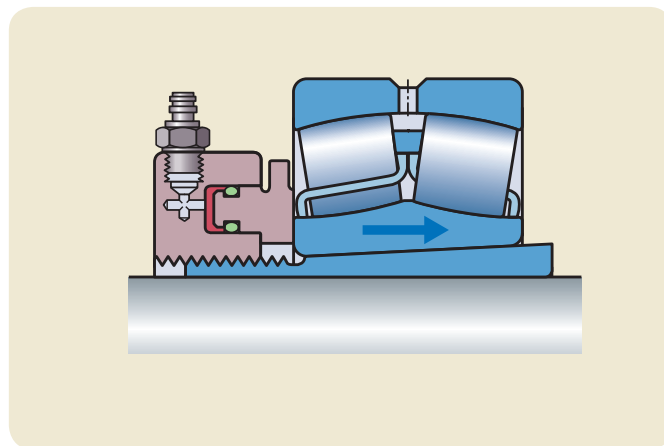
Rodamiento montado sobre un manguito de fijación que se extrae y se desliza entre el rodamiento y el eje.
